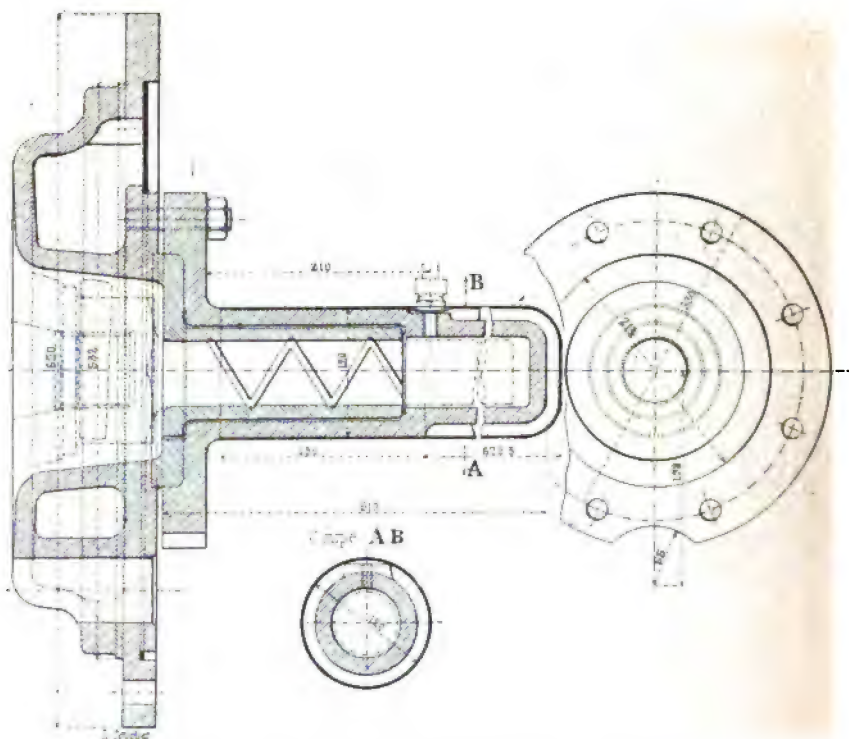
à 136. — Fourreau de contre-tige de piston de locomotive type 35 de l'État belge.
